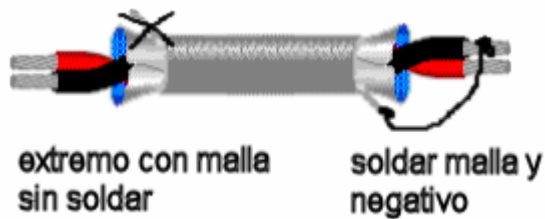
Forma especial de soldado del cable Belden 8451 Fuente: <http://www.lcardaba.com/files/cables.pdf>
